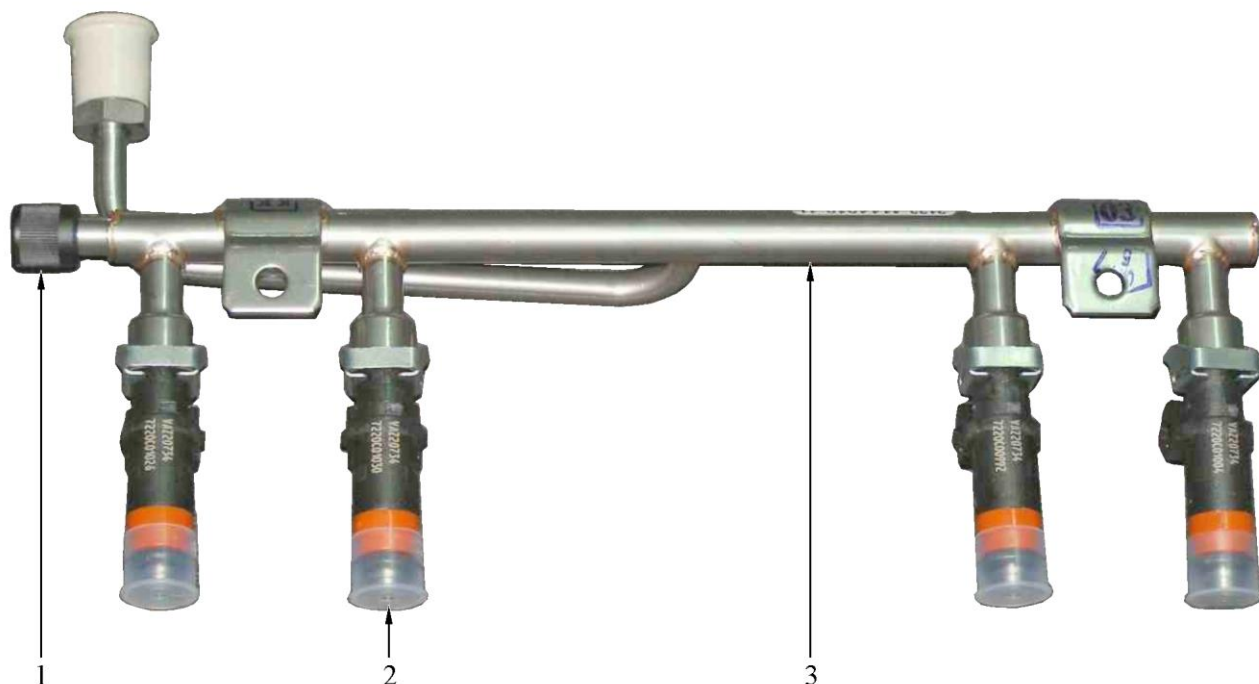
Рампа форсунок в сборе: 1 - штуцер для контроля давления топлива; 2 - форсунка; 3 - рампа форсунок
